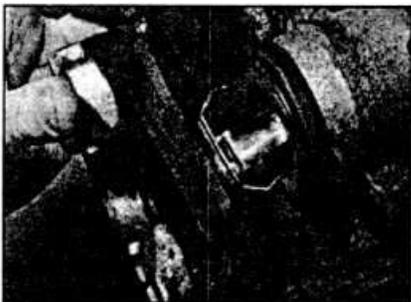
Снятие внутренней колодки с корпуса поршня.
